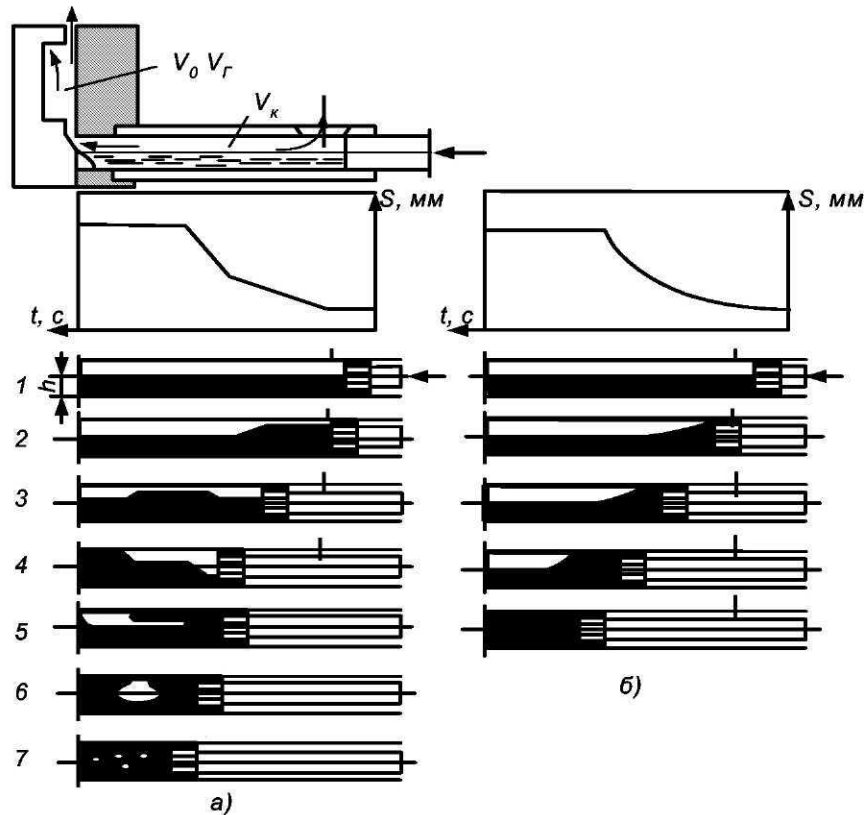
Схема удаления воздуха и газов из пресс-формы и пресс-стакана
